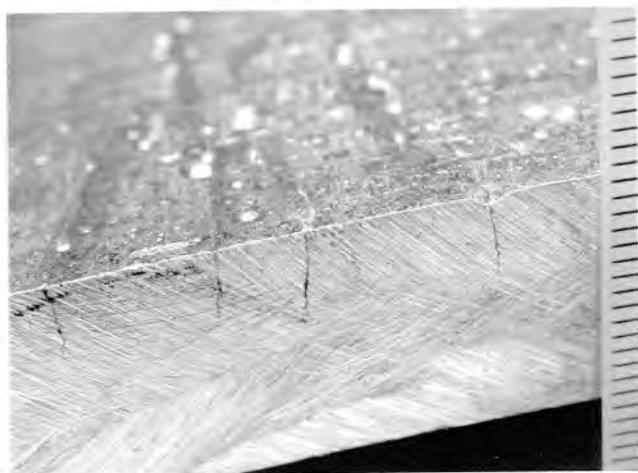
Закат – прикатанный продольный выступ – в основном металле трубы, выходящий на кромку детали в стыковом сварном соединении трубопровода
